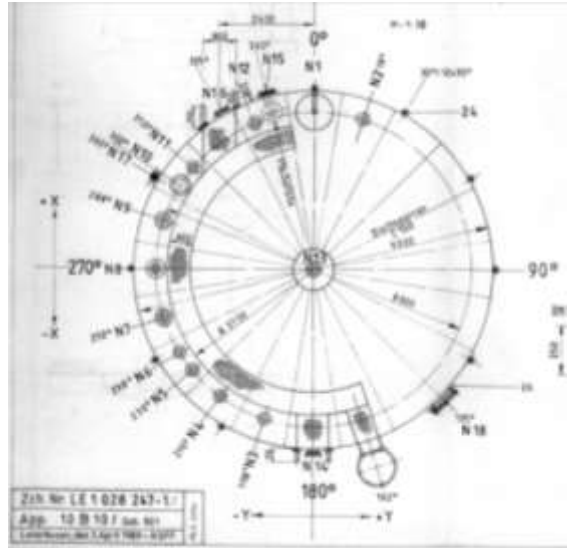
Covestro., plano vista planta de tanques MDA-206 anilina y MDA-81 formalina.
